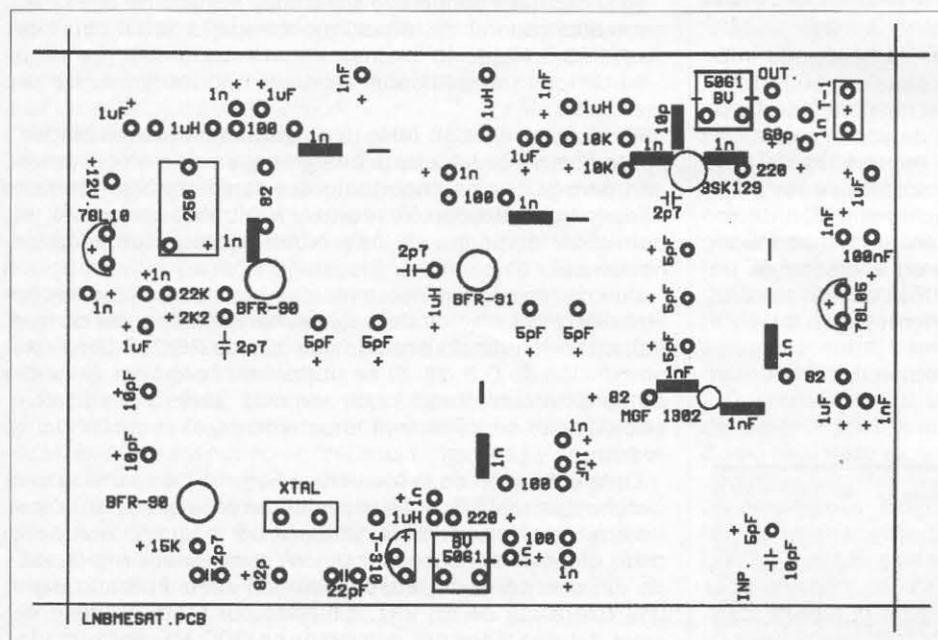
Disposición de componentes en la placa de circuito impreso.
